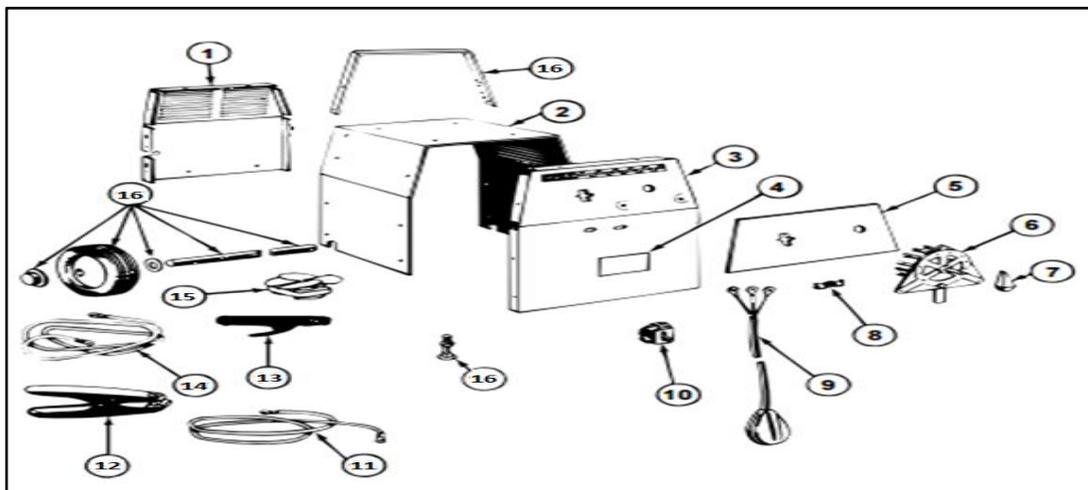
Diagrama de partes, máquina de soldadura, AC-225-GLM. (LINCOLN ,2001)
